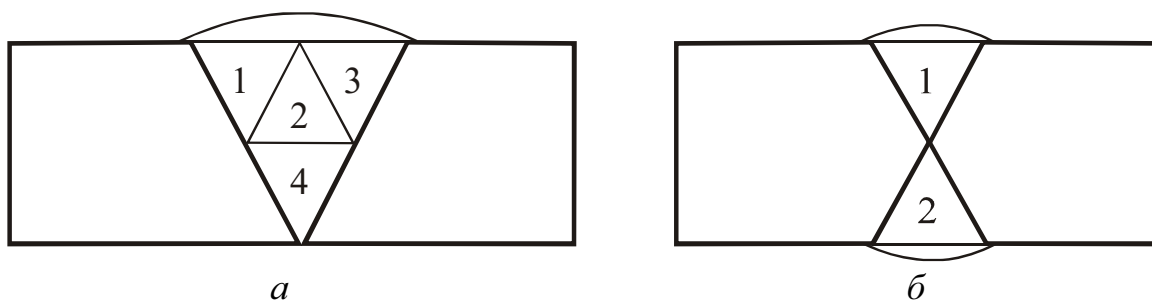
Объём наплавленного металла стыкового соединения:
